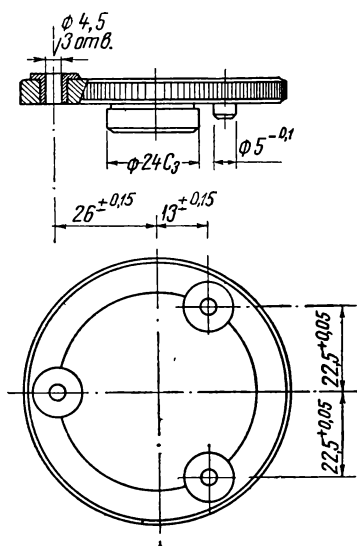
Кондуктор для сверления отверстий в плато проекторов К-25 и К-101 для установки унифицированного узла главного вала
